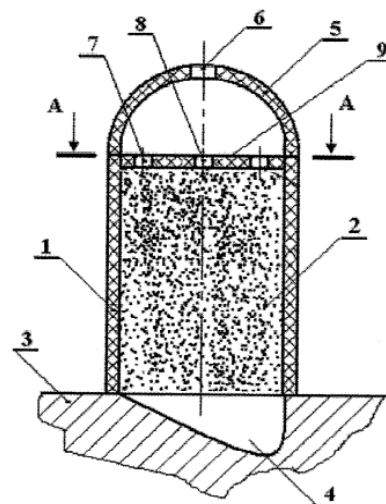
Устройство для ремонта деталей с открытыми поверхностными дефектами
